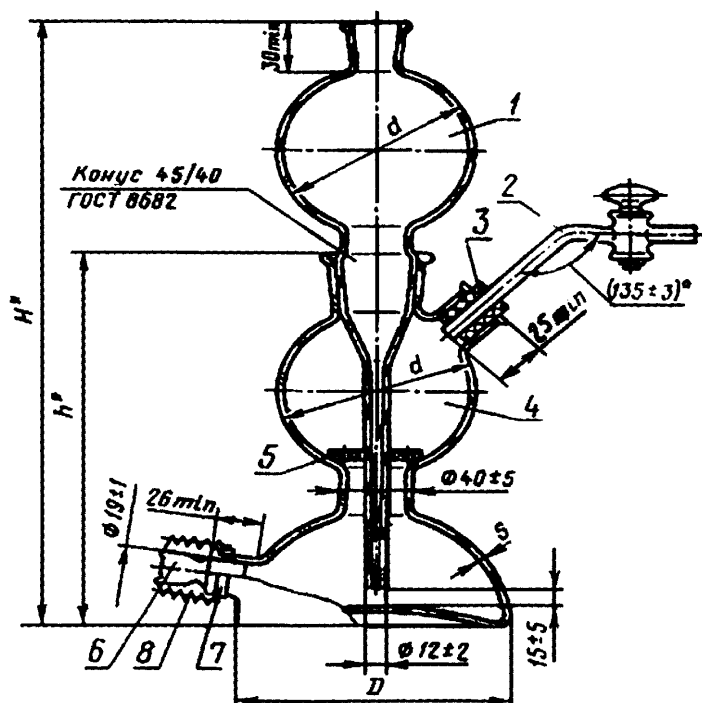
Аппарат Киппа: 1 — воронка; 2 — трубка отводная с краном; 3 — пробка резиновая; 4 — реактор; 5 — вкладыш; 6 — пробка стеклянная; 7 — скоба крепления; 8 — пружина.
